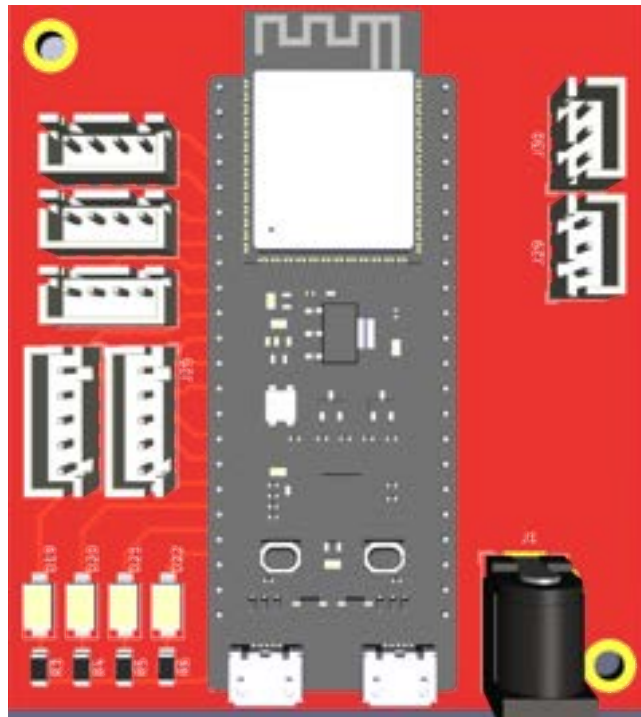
Diseño 3D de la PCB del robot cartesiano.
